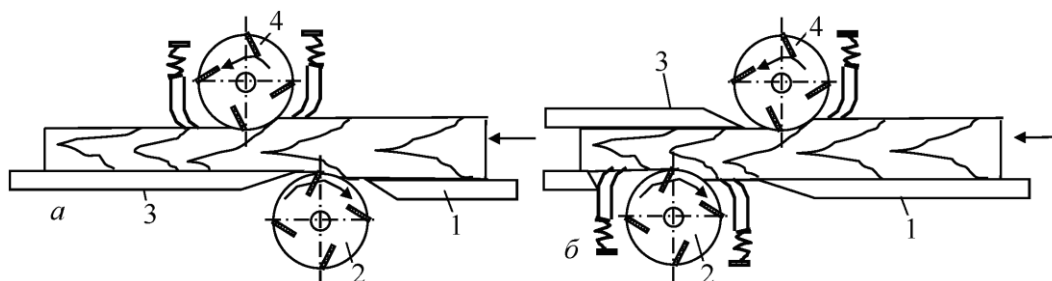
Схеми двостороннього фрезерування: *а* - фугувально-рейсмусова; *б* – дворейсмусова
